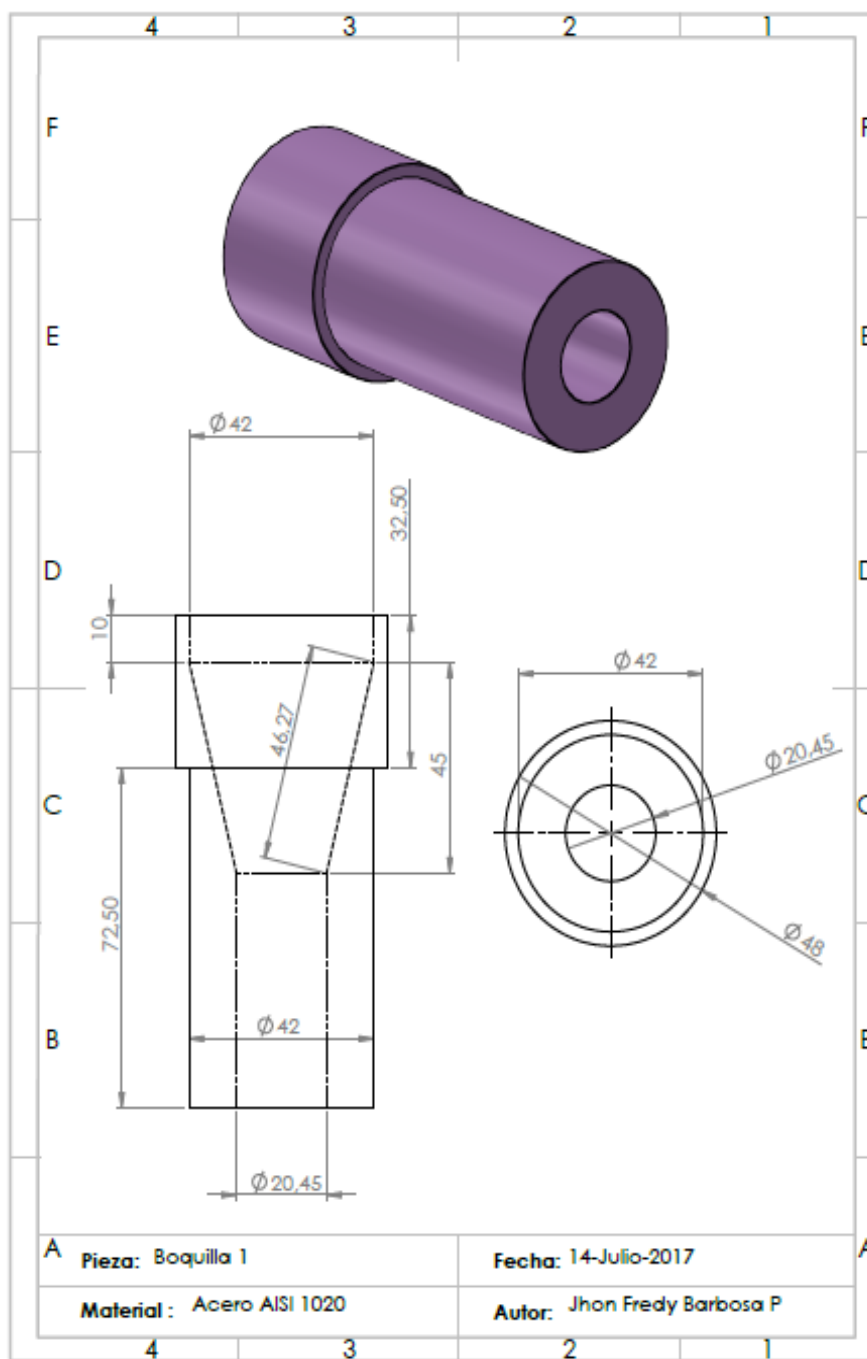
Plano de la parte 1 de la boquilla de extrusión.
